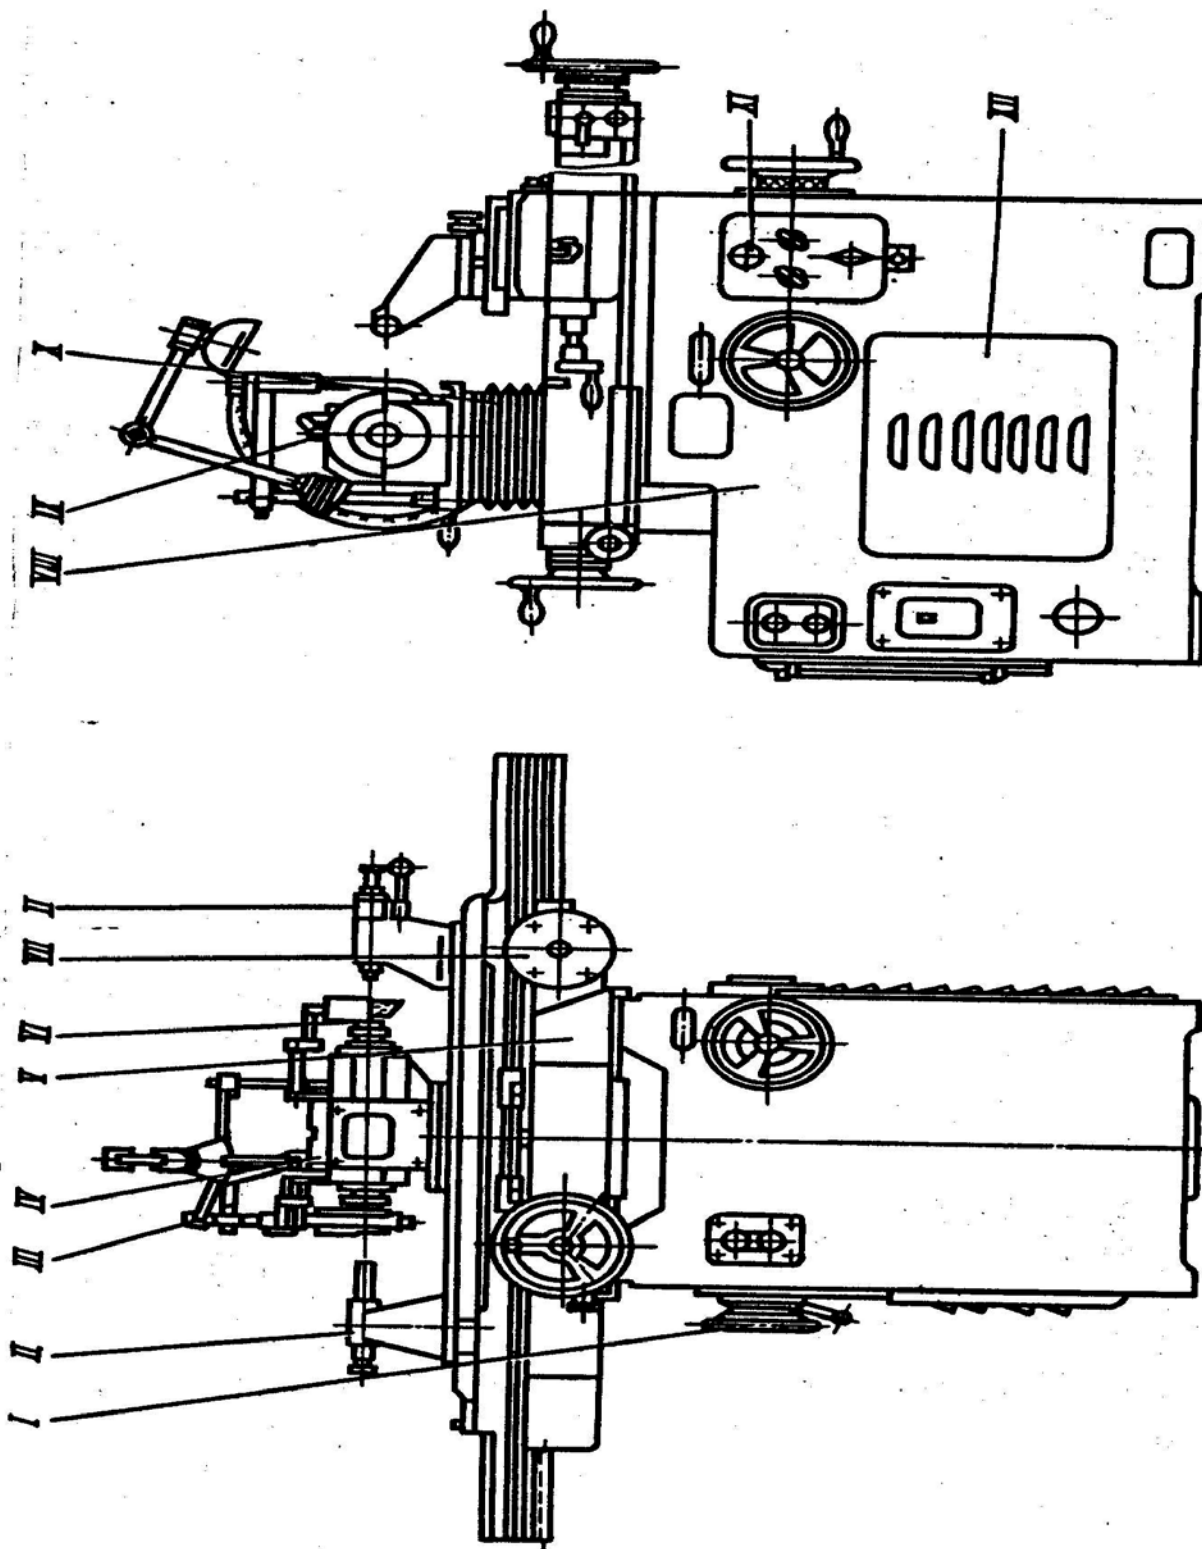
Общий вид универсального заготовочного станка модели 3B642
